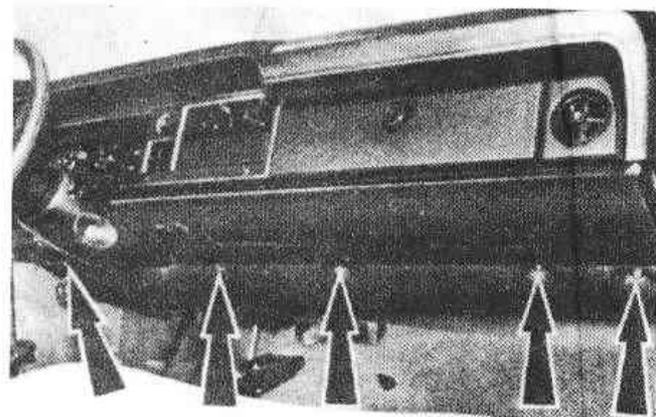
Расположение винтов крепления нижней декоративной панели щитка приборов (Разд.16)
